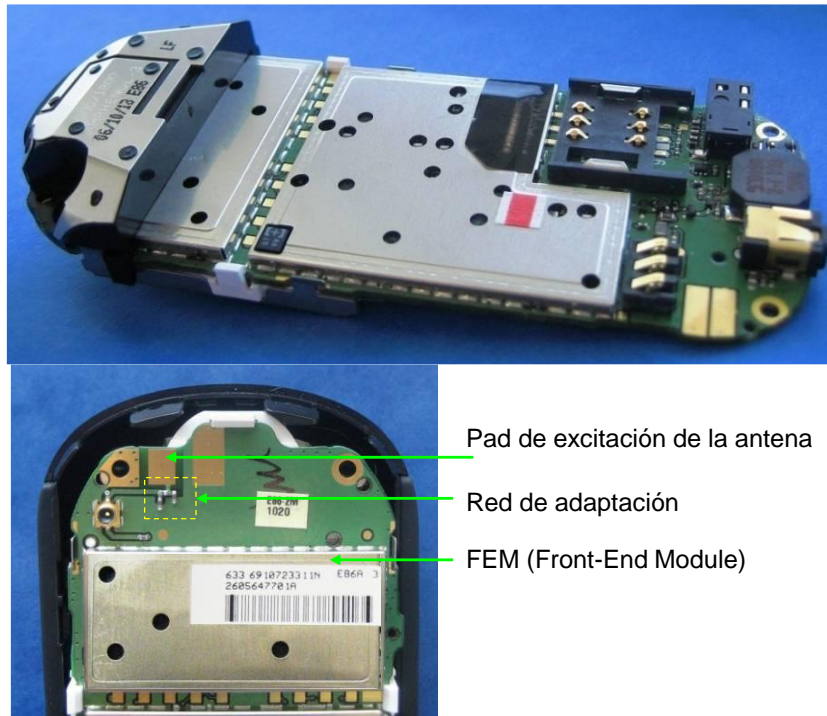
Teléfono móvil que muestra la antena (extremo izquierda) y detalle de la PCB (Printed Circuit Board).
